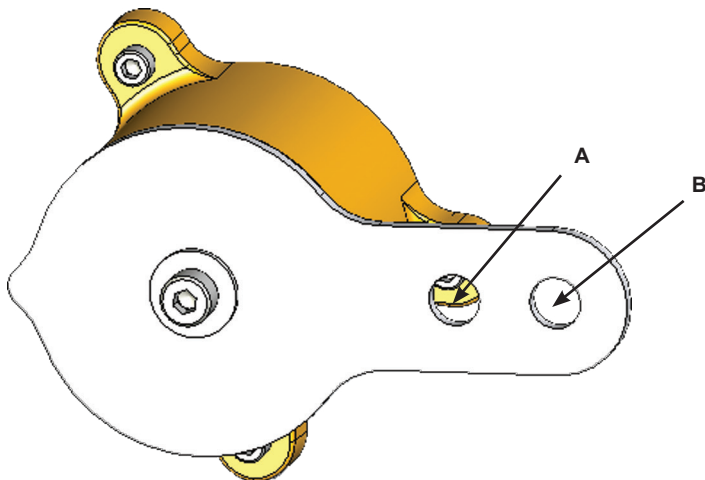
Palanca del SVi1000 instalada a un ensamble IM
